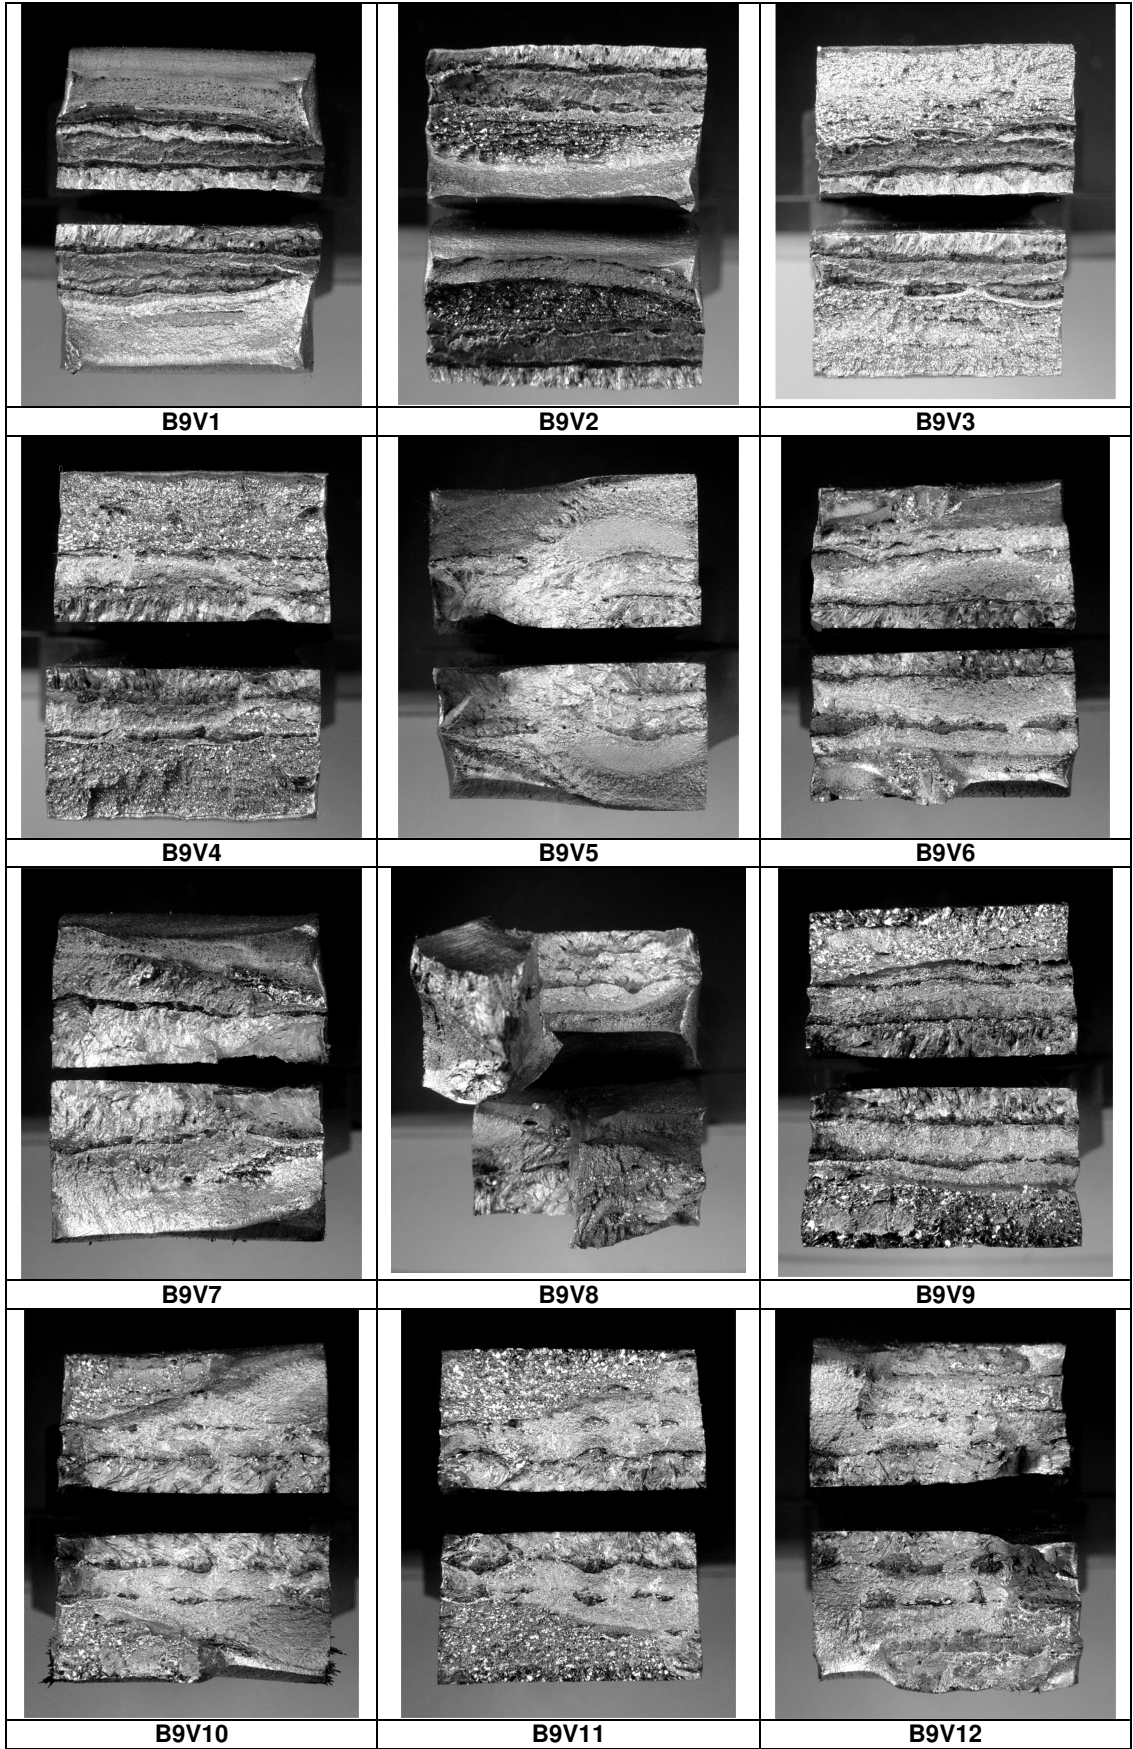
SMAW kaynaklı bağlantının fraktografaları (V9).
